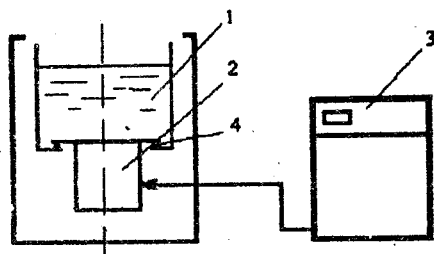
Схема ультразвуковой установки для очистки изделий
